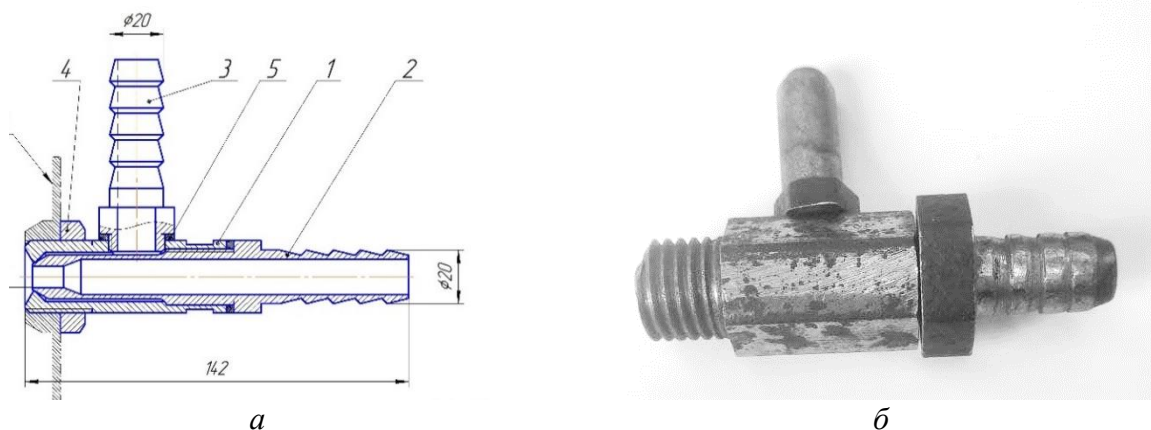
Схема разработанной форсунки (а) и общий вид изготовленного экспериментального образца форсунки (б): 1– корпус; 2– шток; 3– штуцер; 4– контргайка; 5– прокладка
